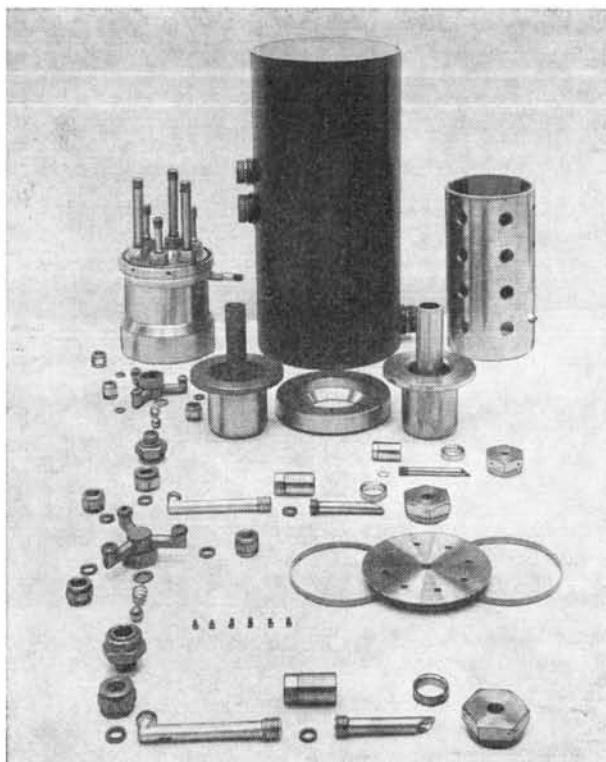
Vue éclatée du moteur « OPM-1 ». Fig. 8. Despiece del motor OPM-1.
